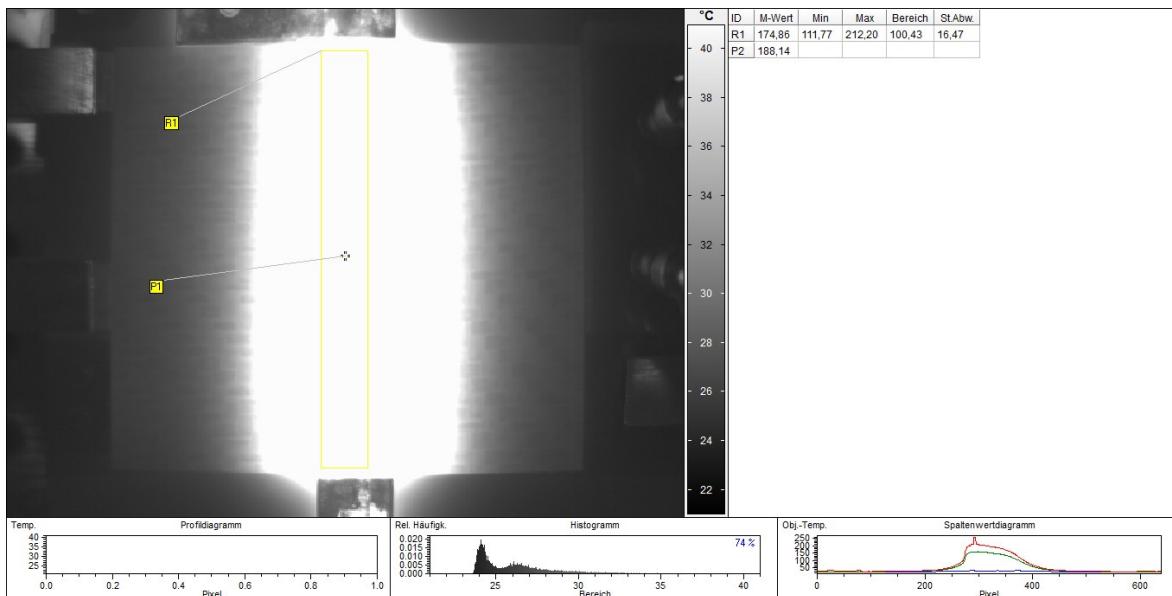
Wärmeausbreitung im Schweißnahtbereich bei der Schweißung P100: eingespannte Fügepartner nach Schweißung.
